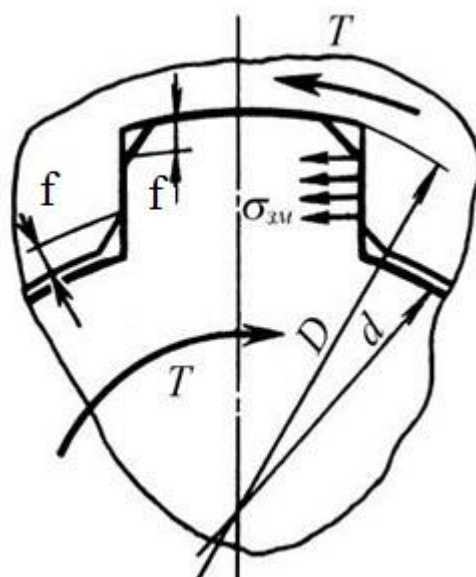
Розрахункова схема прямобічного шліцевого з'єднання
